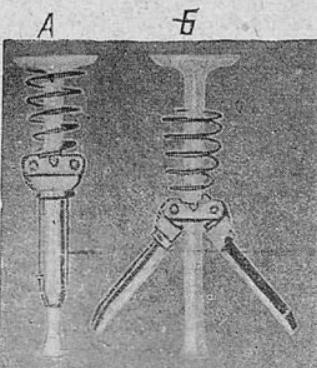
Втулка с пружинкой для притирки клапанов в двигателе ГАЗ
